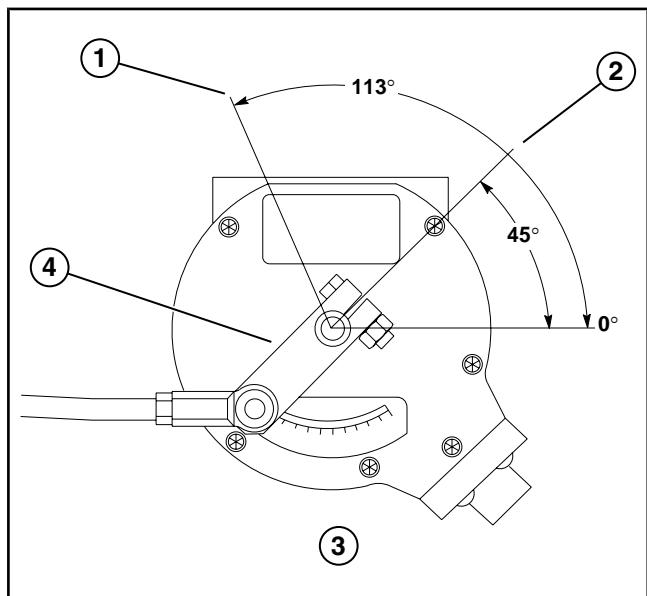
Углы установки концевого вала регулятора скорости
